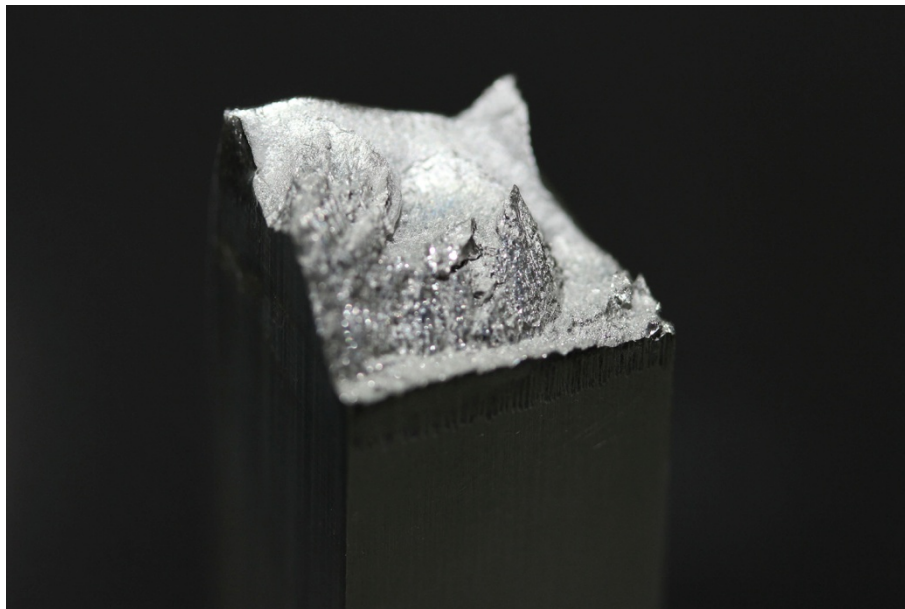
12 - CP 11 com foco mais interno na superfície de fratura.
